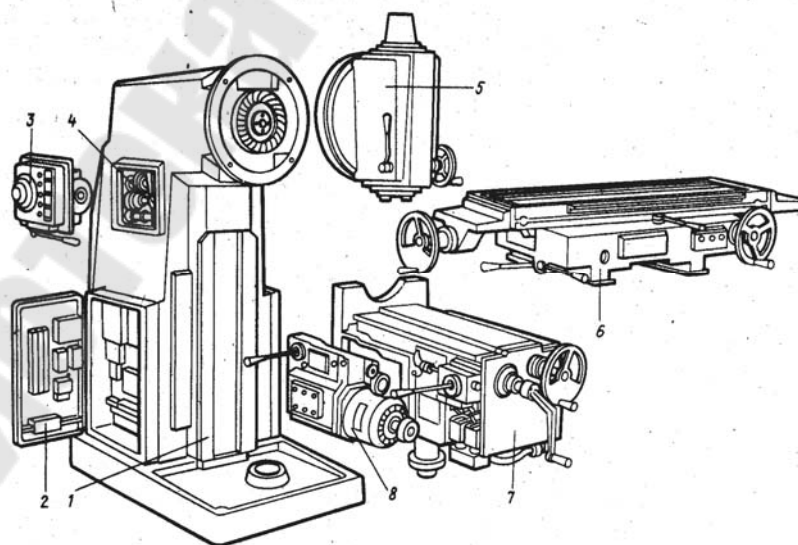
Основные части консольно-фрезерного станка модели 6Р13Б
